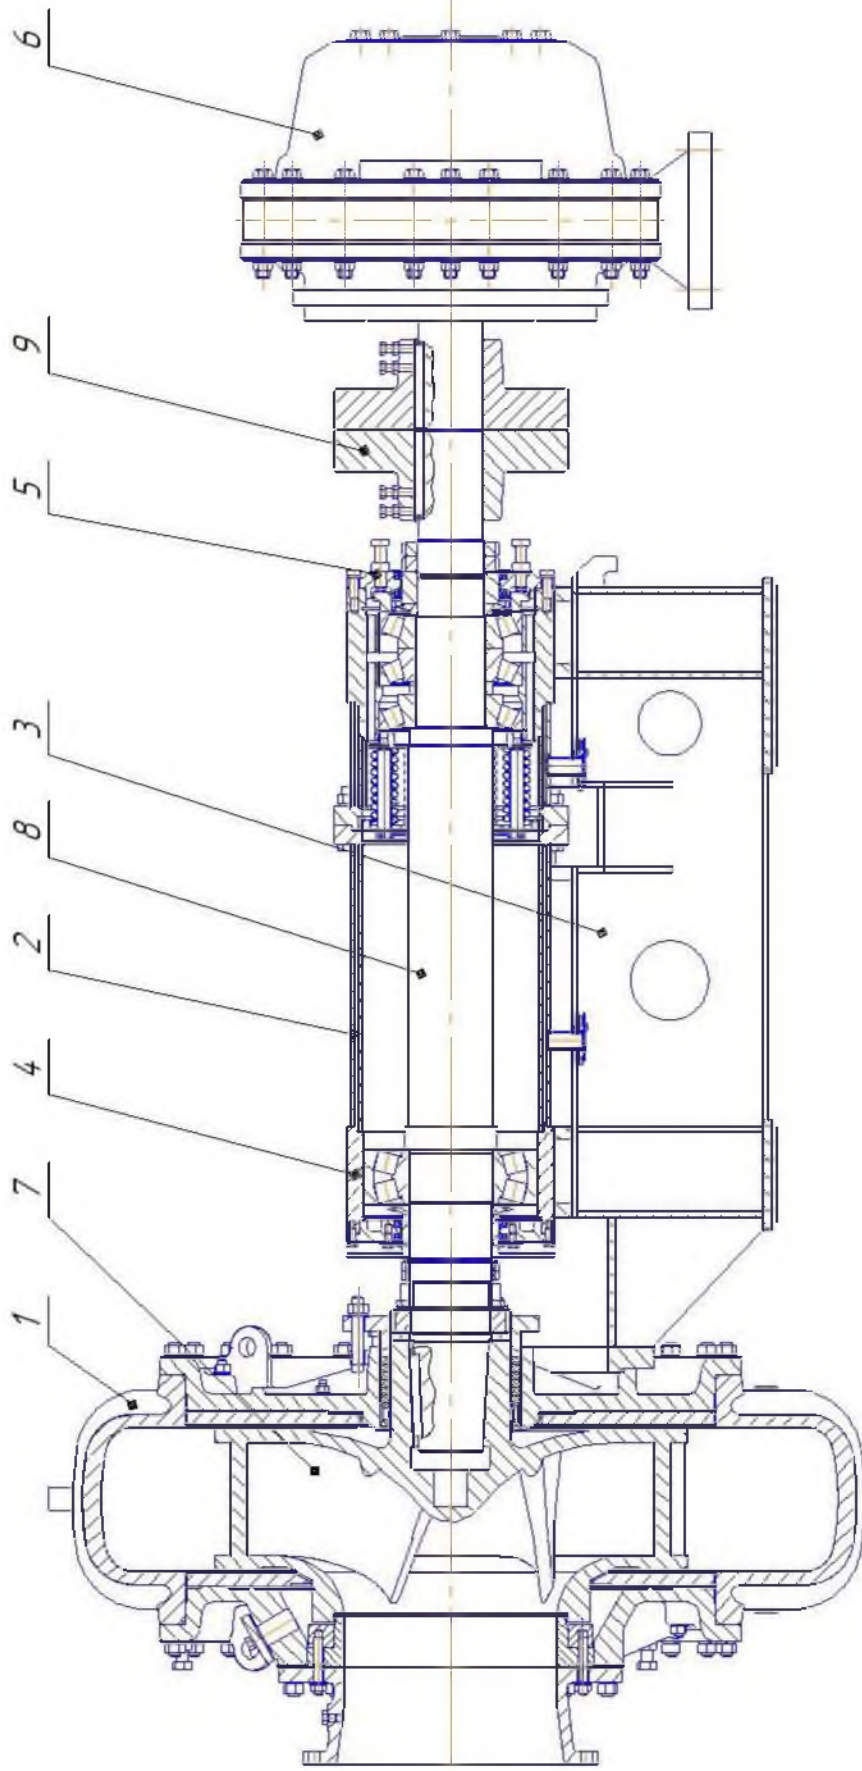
Оновлена конструкція системи обертання робочого колеса
